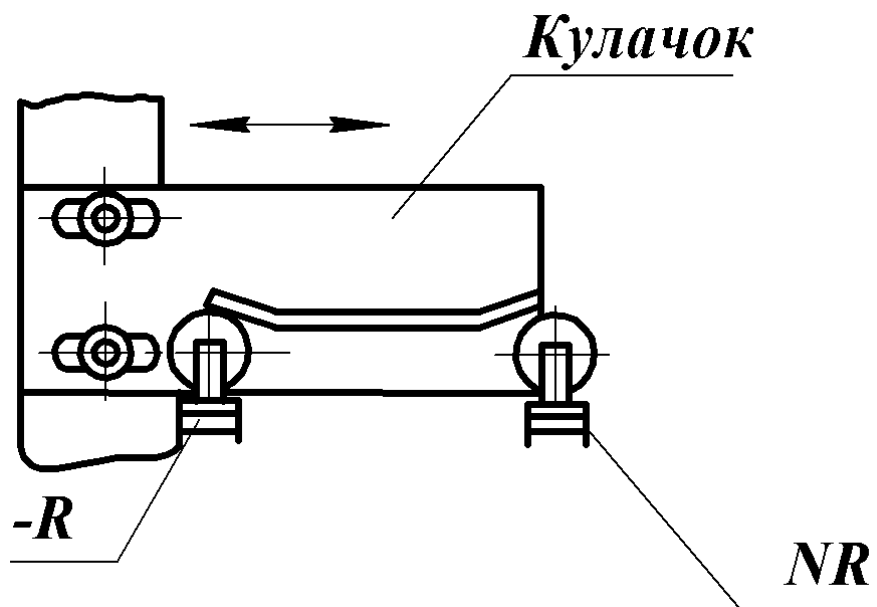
Схема расположения кулачка и микропереключателей положений по координате R
